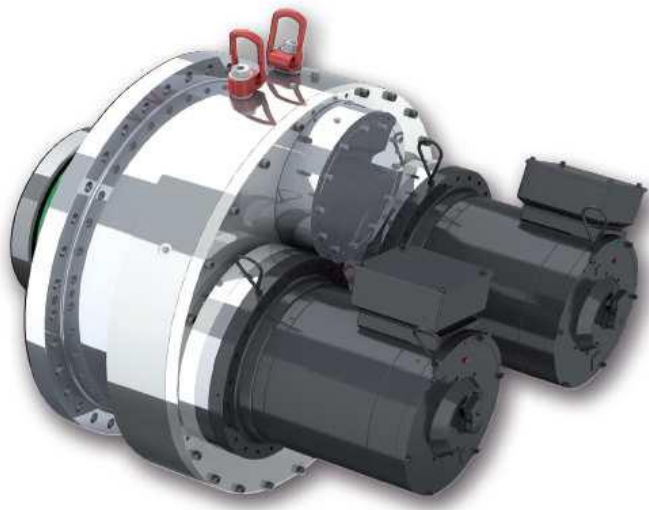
Pohonná jednotka GOIZPER Complete press drive [35]
